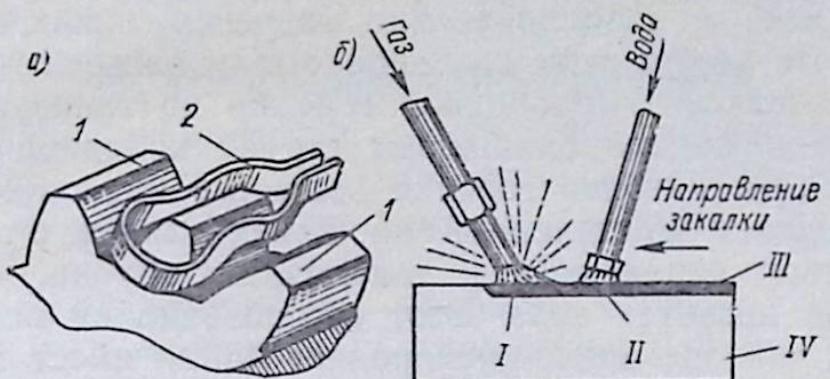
Способы нагрева при поверхностной закалке стали: *а* — токами высокой частоты; *б* — ацетилено-кислородным пламенем:
